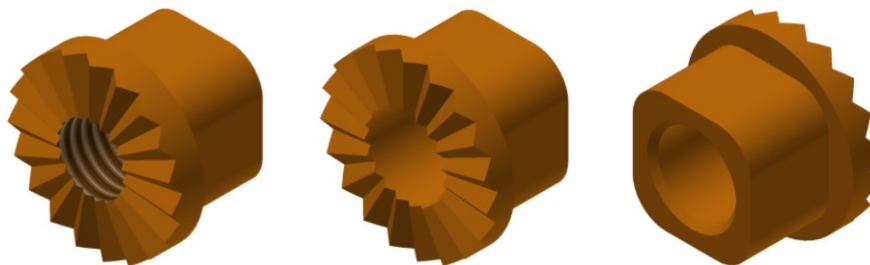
Spojení vložek s vícehranem a rameny přípravku
